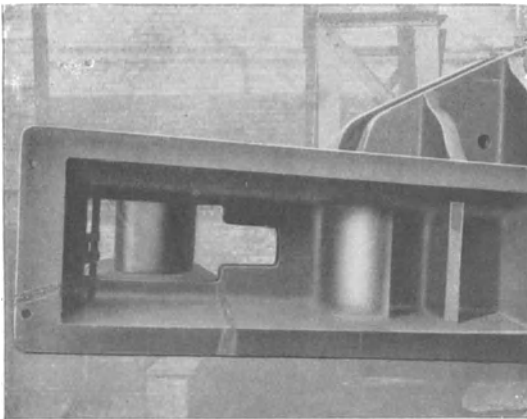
Schmiedepressenrahmen, fertig geschweißt, Innenansicht.
